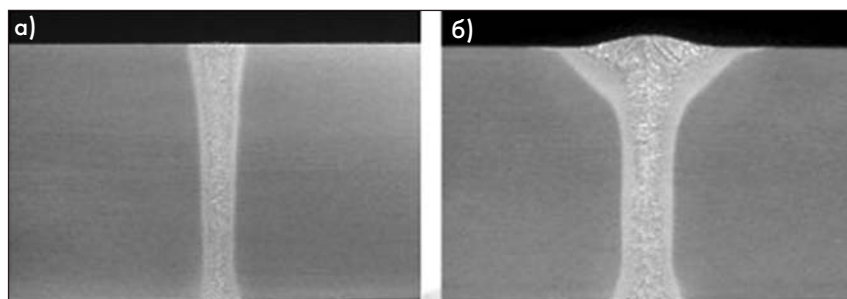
Микрошлифы сварного соединения, выполненного лазерной сваркой (а) и гибридной лазерно-дуговой сваркой (б)
